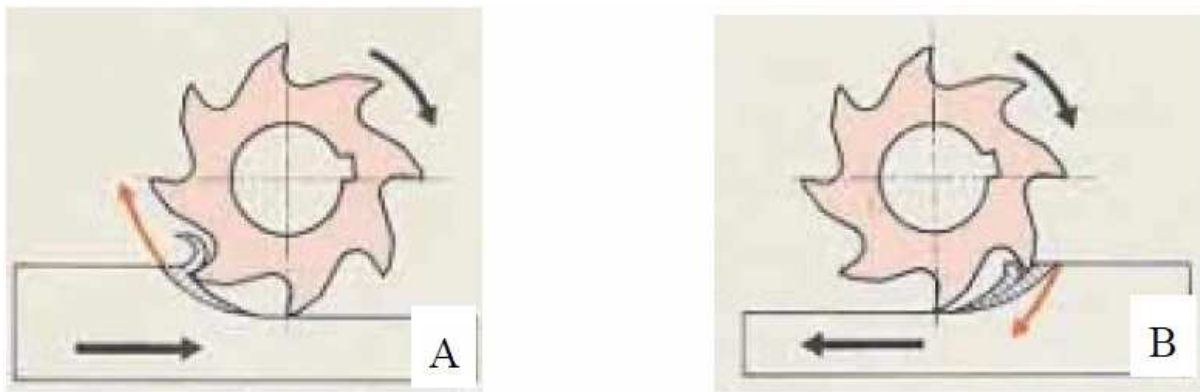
Fresagem cilíndrica discordante (A) e concordante (B) [9]
